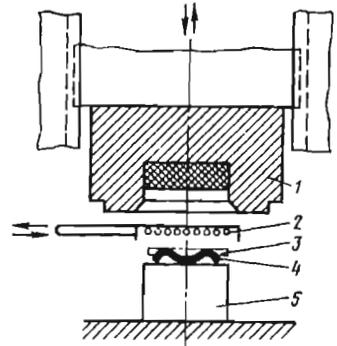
Оснастка для динамической штамповки деталей из малопластичных материалов с предварительным нагревом:
